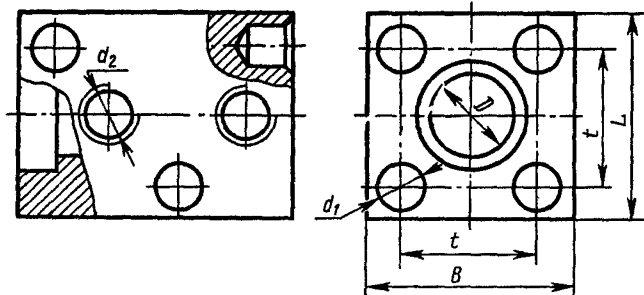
Модуль корпусных деталей комплекса УСПО
